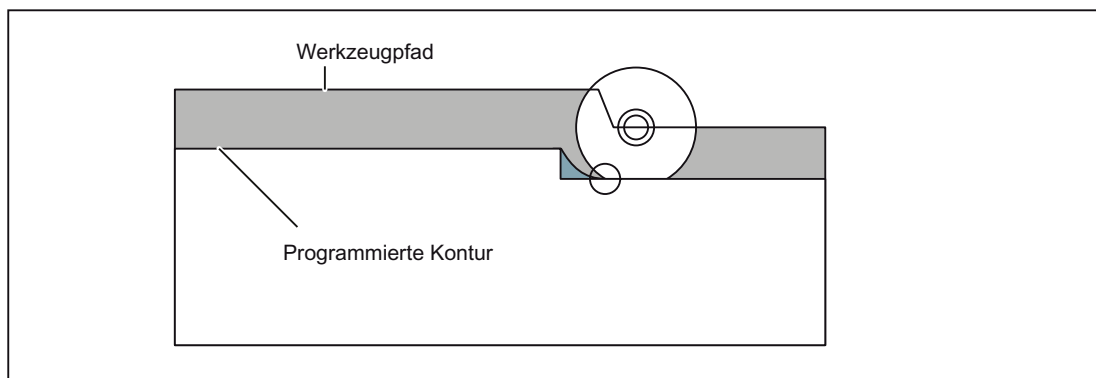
Konturzug kürzer als der Werkzeugradius
